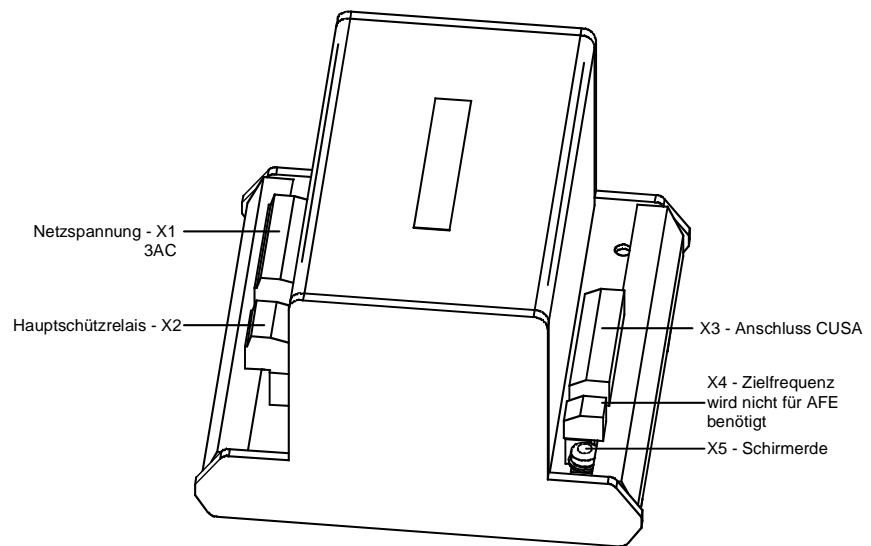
Ansicht der Optionsbaugruppe VSB
